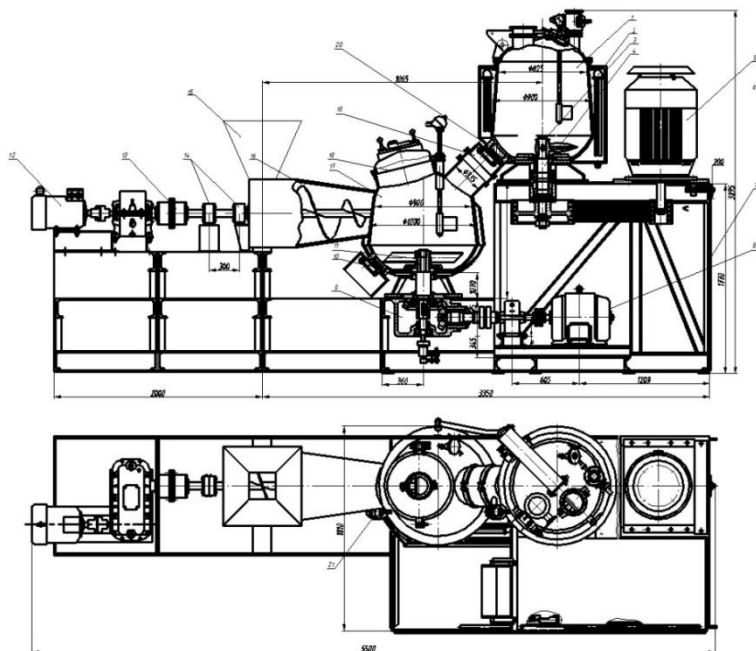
Двухкамерный высокотемпературный вакуум смеситель:
